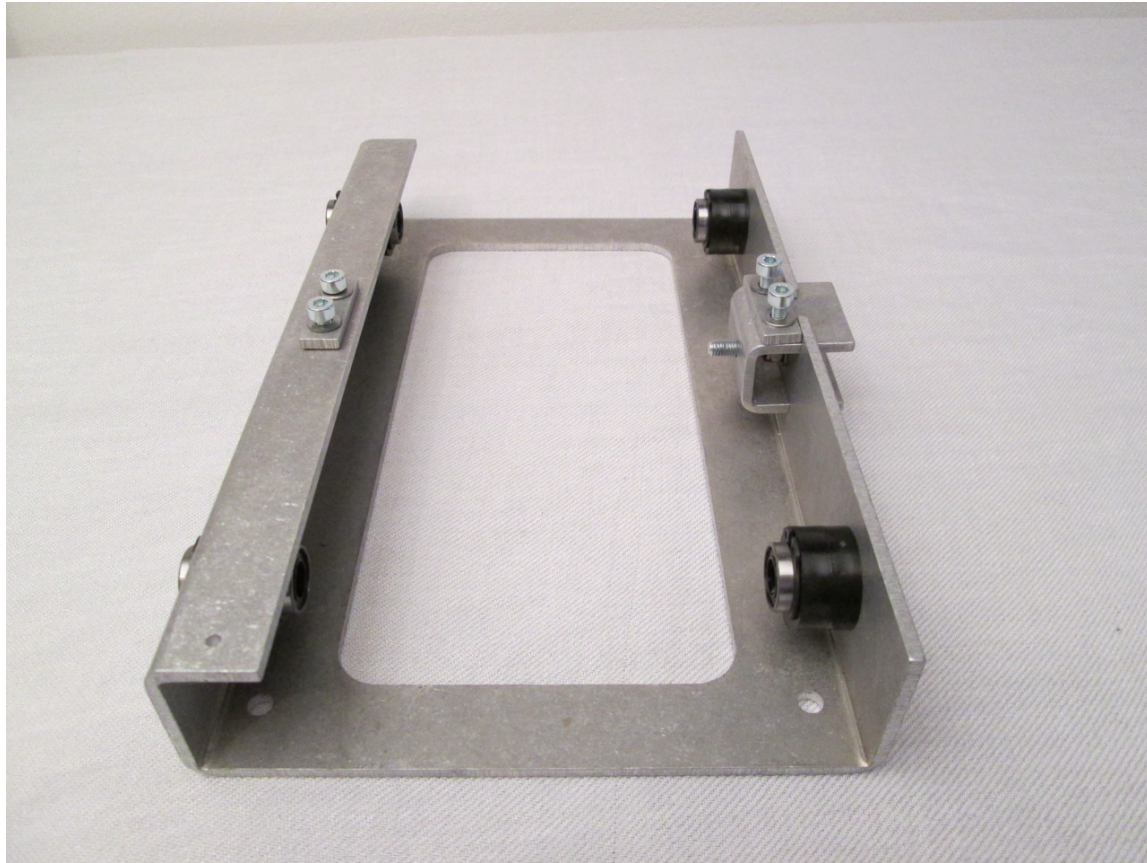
Detailansicht: Y-Riemenspanner und Y-Riemenklemme Montage Teil 2
